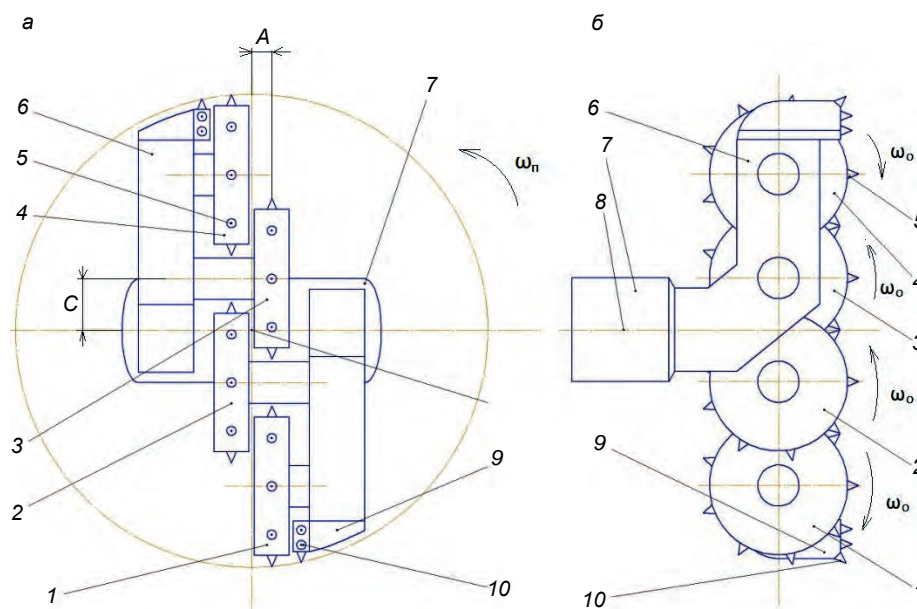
Планетарно-дисковый исполнительный орган, реализующий перекрестную схему разрушения калийного массива. а – вид спереди; б – вид сбоку.
